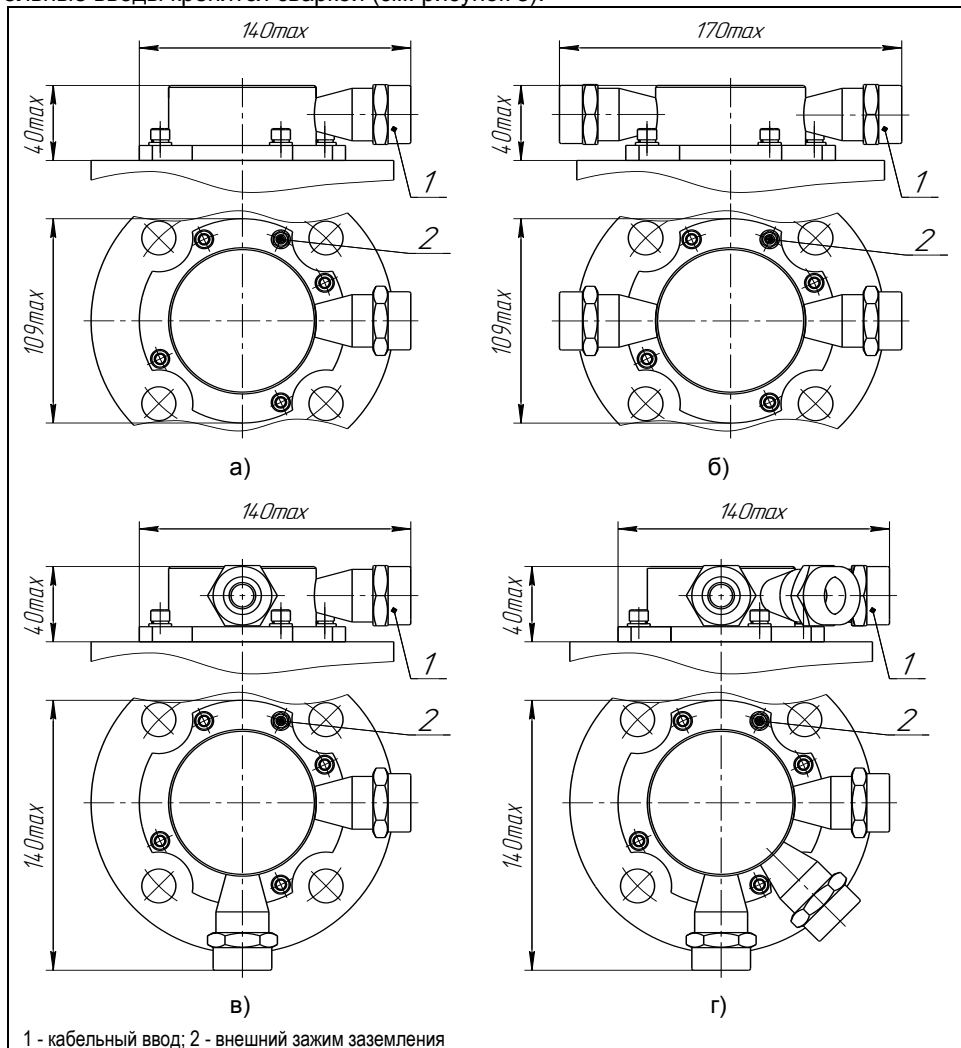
Варианты исполнения корпуса из нержавеющей стали:
